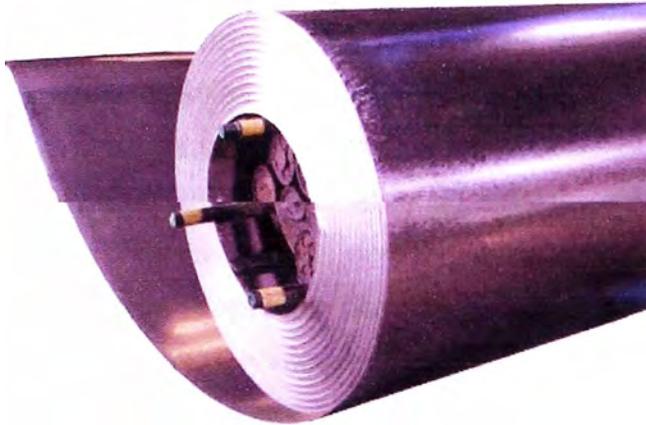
Bobina de Acero estructural empaquetados en bobinas de 5 ton.
